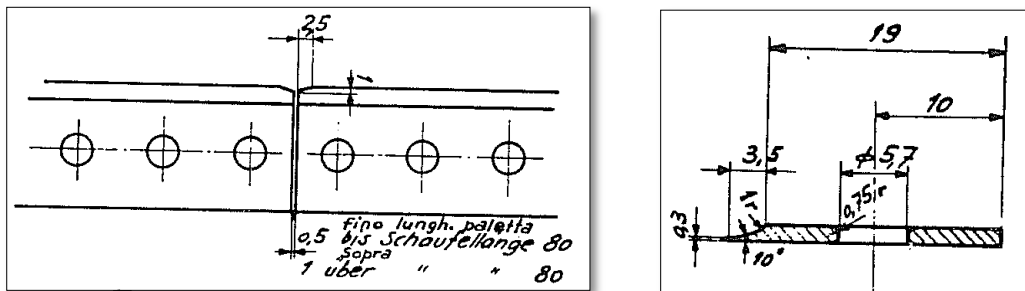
dimensioni del bendaggio del 4° stadio della macchina n° 3.
